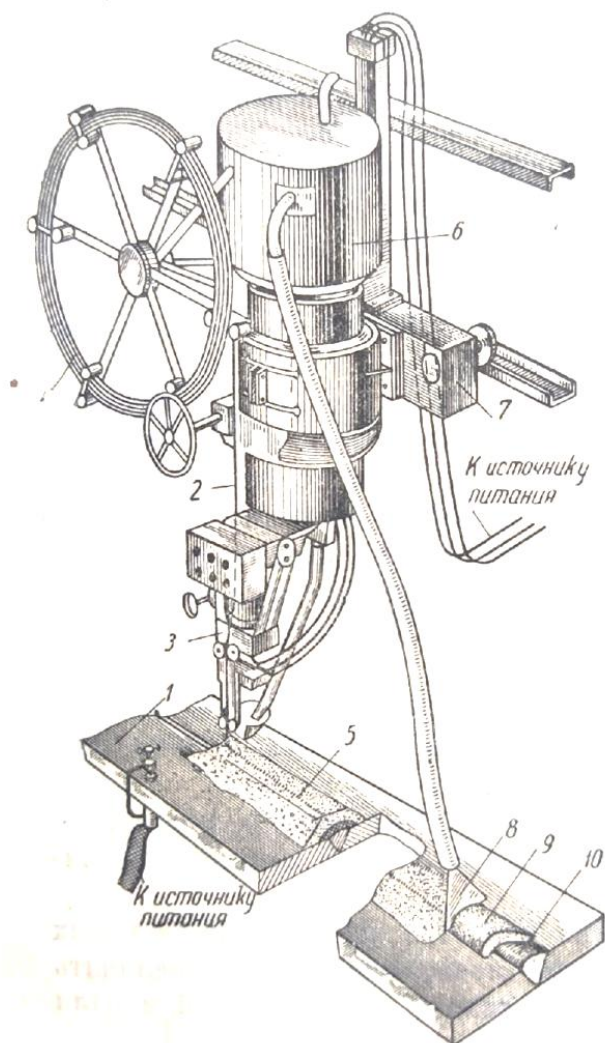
Схема процесса автоматической сварки под флюсом [1]
